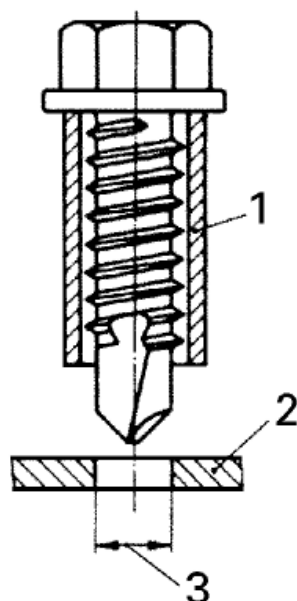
Приспособление для проверки диаметра просверленного отверстия
